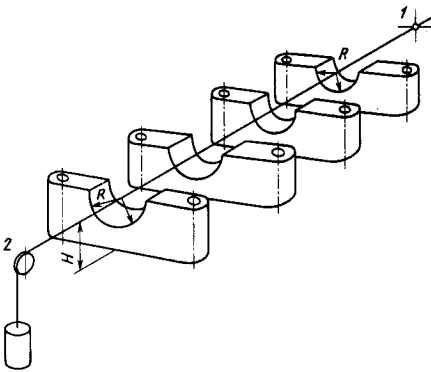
Схема установки корпусов подшипников по струне: 1 — точка закрепления струны; 2 — блок
